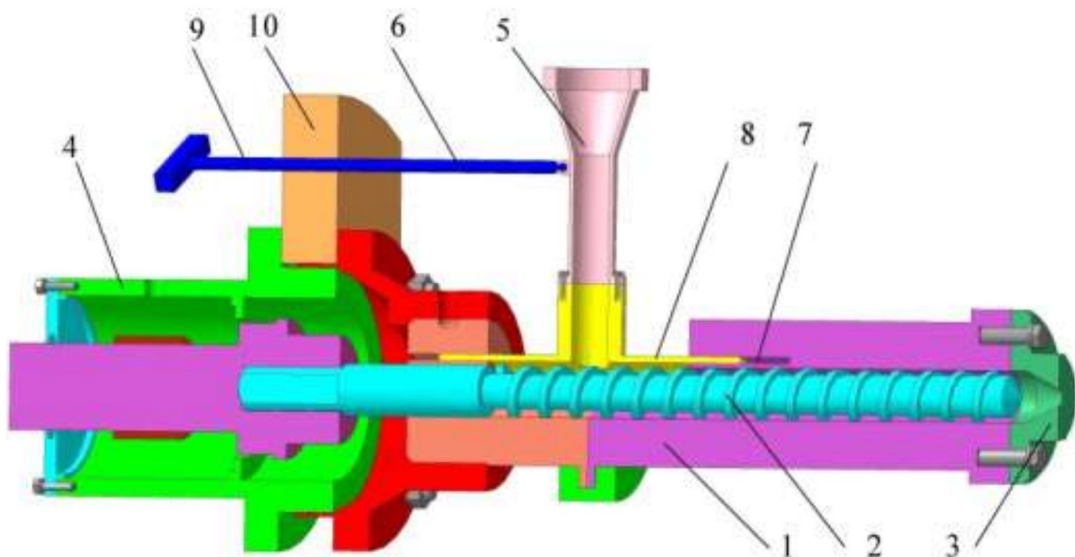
Екструдер для переробки термопластичних матеріалів: 1 - корпус; 2 - шнек; 3 - формуюча матриця; 4 - станина; 5 - завантажувальний патрубок; 6 - шток; 7 - проріз; 8 - напрямна; 9 - хвостовик; 10 - опорна плита
